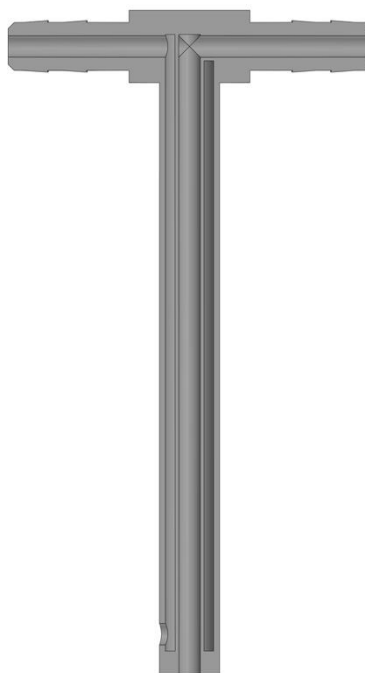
Трубка Пито-Прандтля с плоской поверхностью вокруг отверстия статического напора, образец I, разрез
